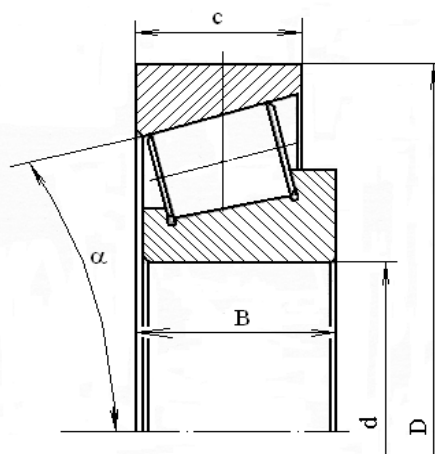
Подшипник роликовый радиально - упорный с коническими роликами
